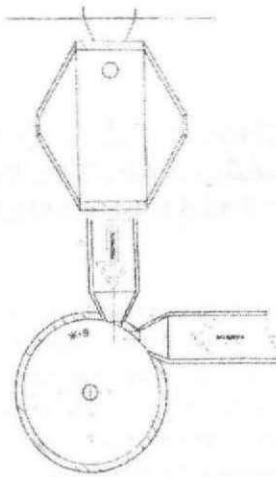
Центробежный двусторонний пневматический распылитель жидкости
